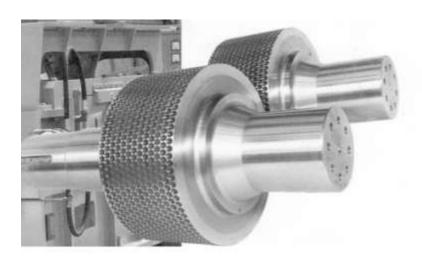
Внешний вид рабочих валков вальцевого пресса
